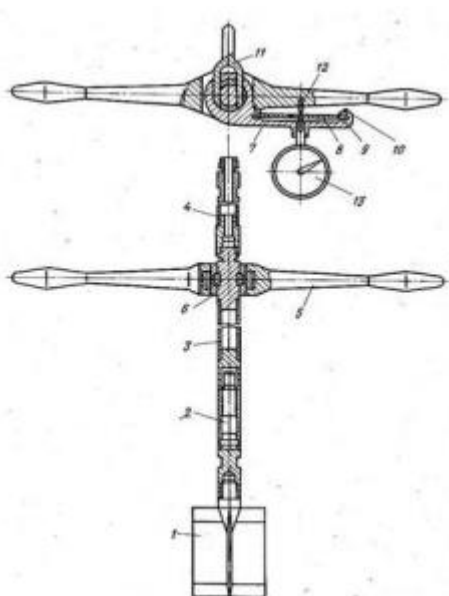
Сдвигомер-крыльчатка СК-10: 1 – крыльчатка; 2 – корпус; 3 – штанга; 4 – втулка крепления; 5 – рукоятка; 6 – втулка; 7 – корпус динамометра; 8 – плоская пружина; 9 – призма; 10 – крепление пружины; 11 – вилка для фиксации корпуса динамометра на штанге; 12 – нажимное устройство; 13 – индикатор часового типа [18]
